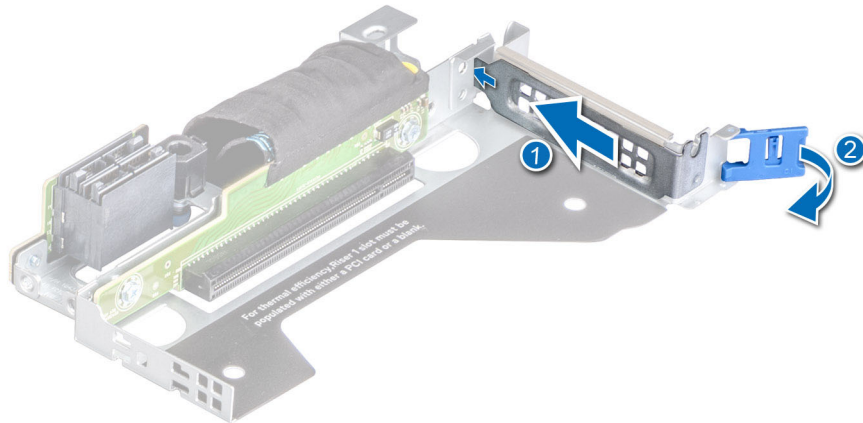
Installation de la plaque de recouvrement sur la carte de montage compacte droite
